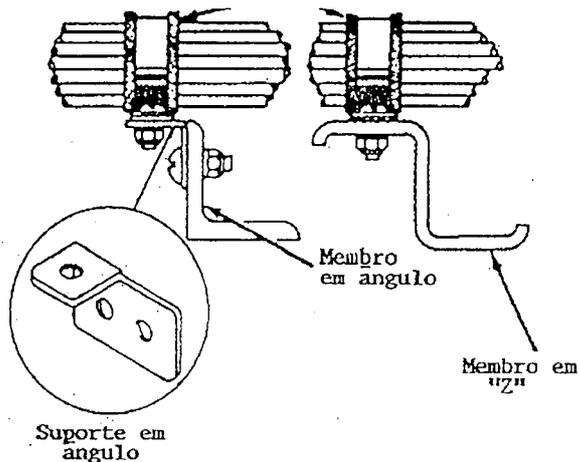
Montagem da braçadeira de cabo na estrutura
